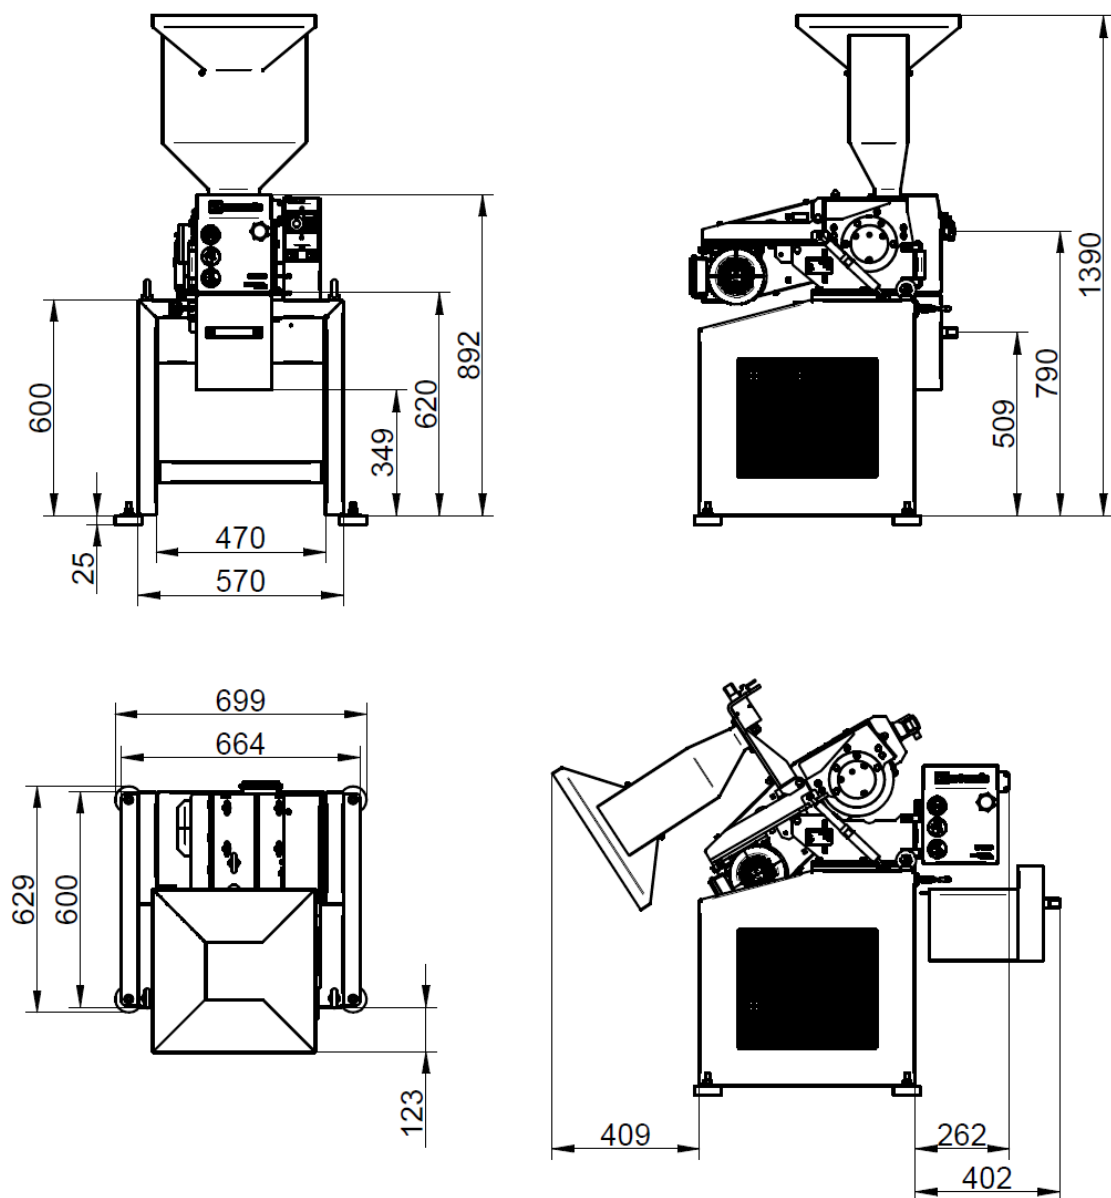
монтажный чертёж Стандартная загрузочная воронка
